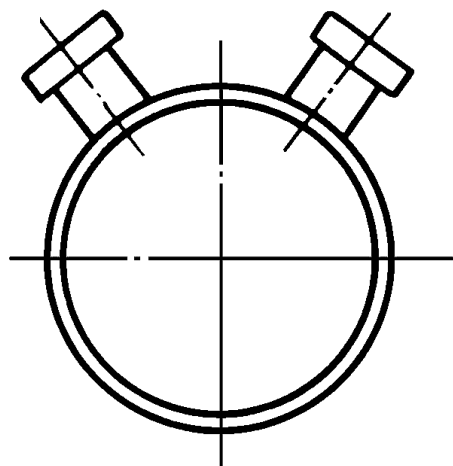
Блок электронагревательный резервуарный БЭР-12
